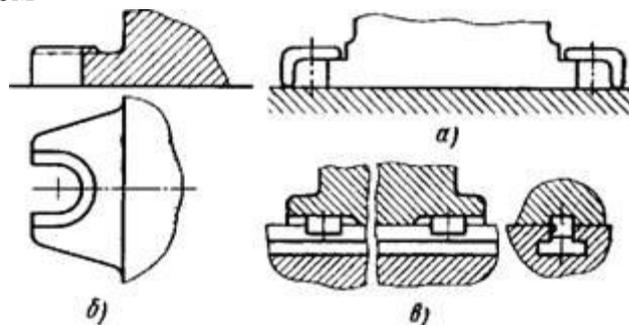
Варианты фиксации и крепления корпуса на столе станка
